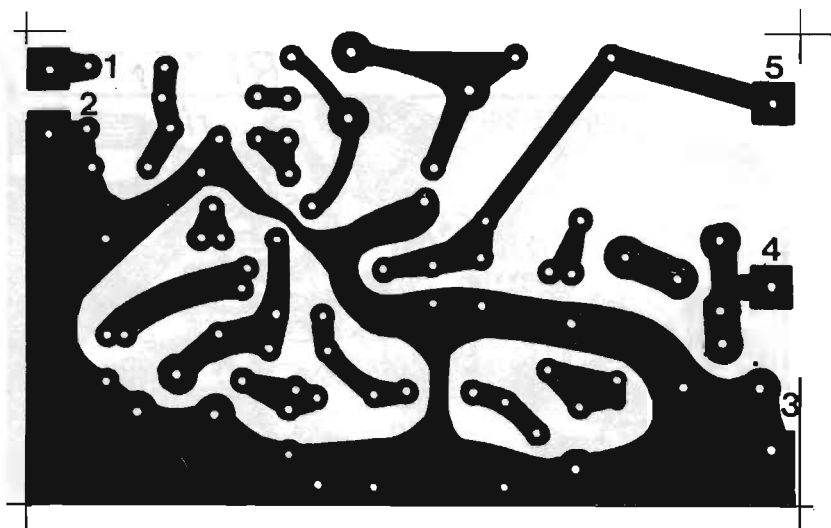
Disegno in grandezza reale del circuito stampato sul quale deve essere composto il modulo elettronico del trasmettitore.
